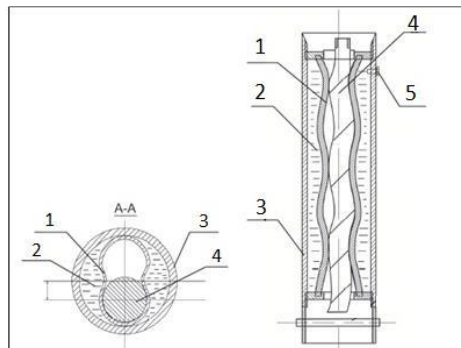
Конструкція ГШНУ із металевим статором:
